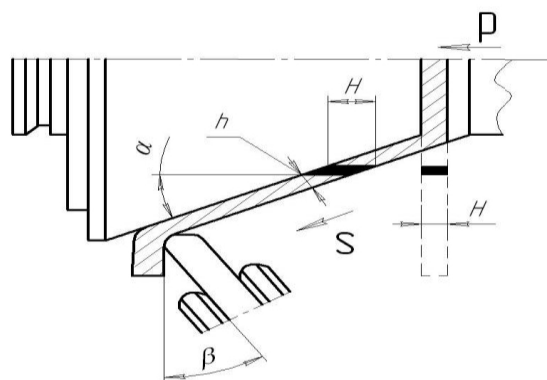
Схема ротационной вытяжки деталей с конической образующей: S – направление подачи
